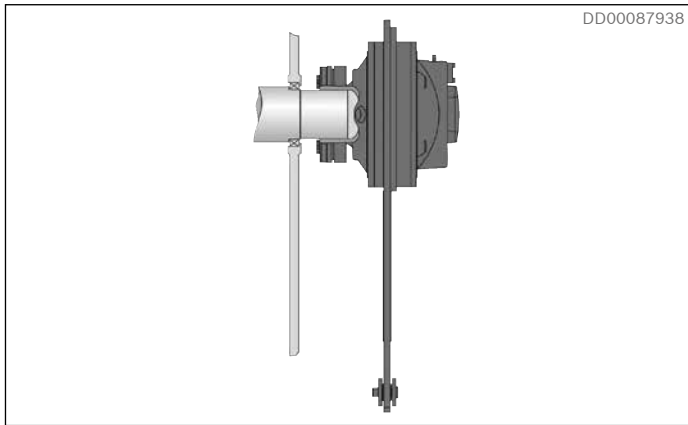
Instalación de brazo de torque del motor con disco compresor.
